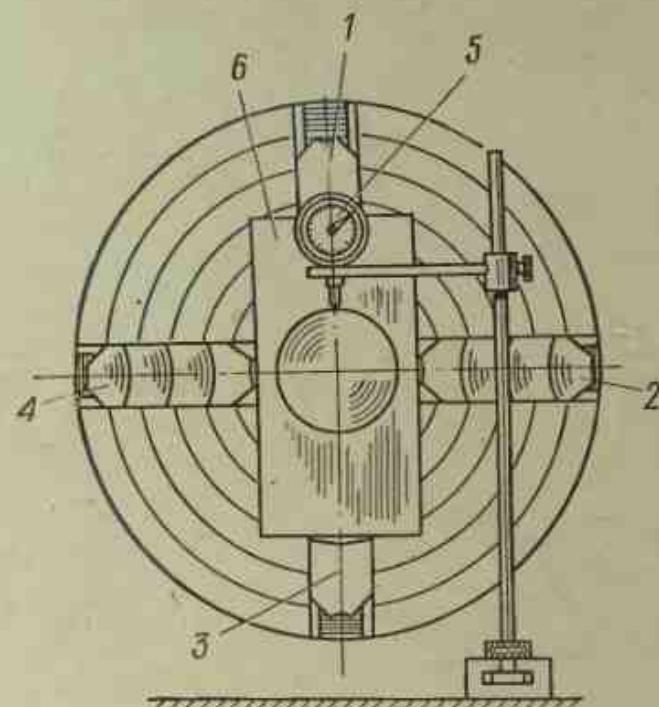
Установка прямоугольной заготовки в четырехкулачковом патроне:
